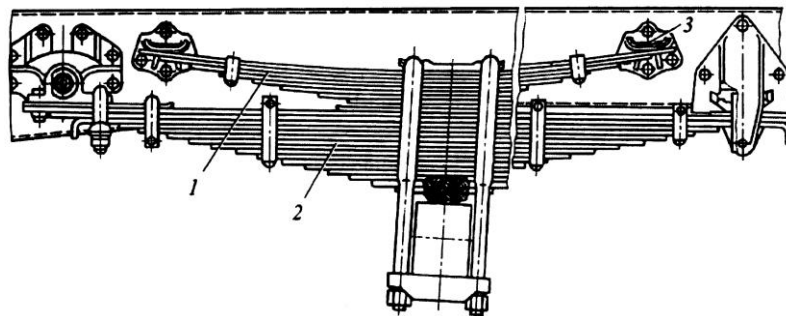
Ресорна підвіска з додатковою ресорою:
